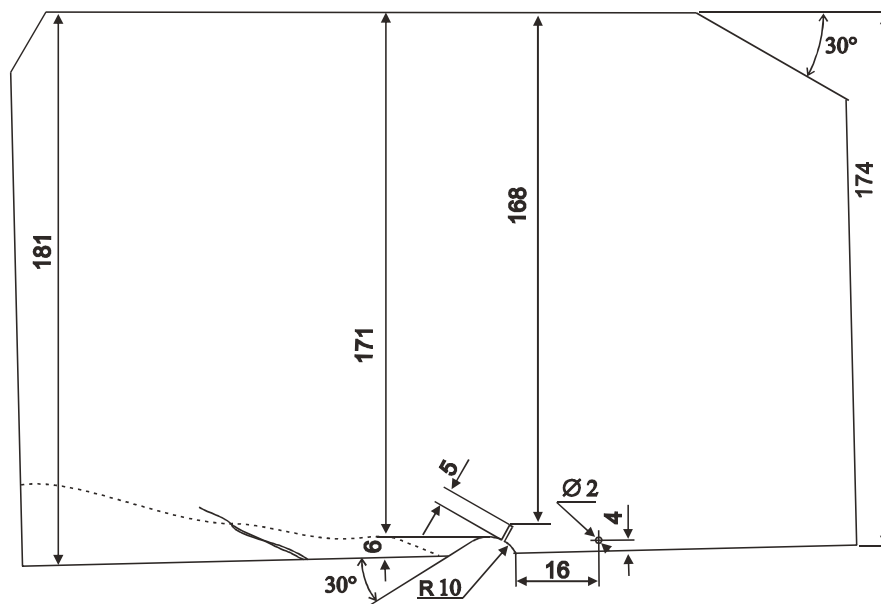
Эскиз образца сварного соединения с естественной трещиной в наплавке.
